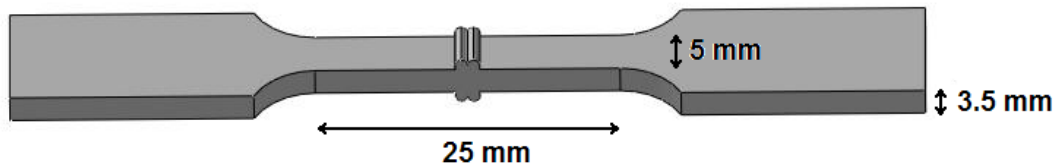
Dimensiones de las probetas para el ensayo de tracción.
